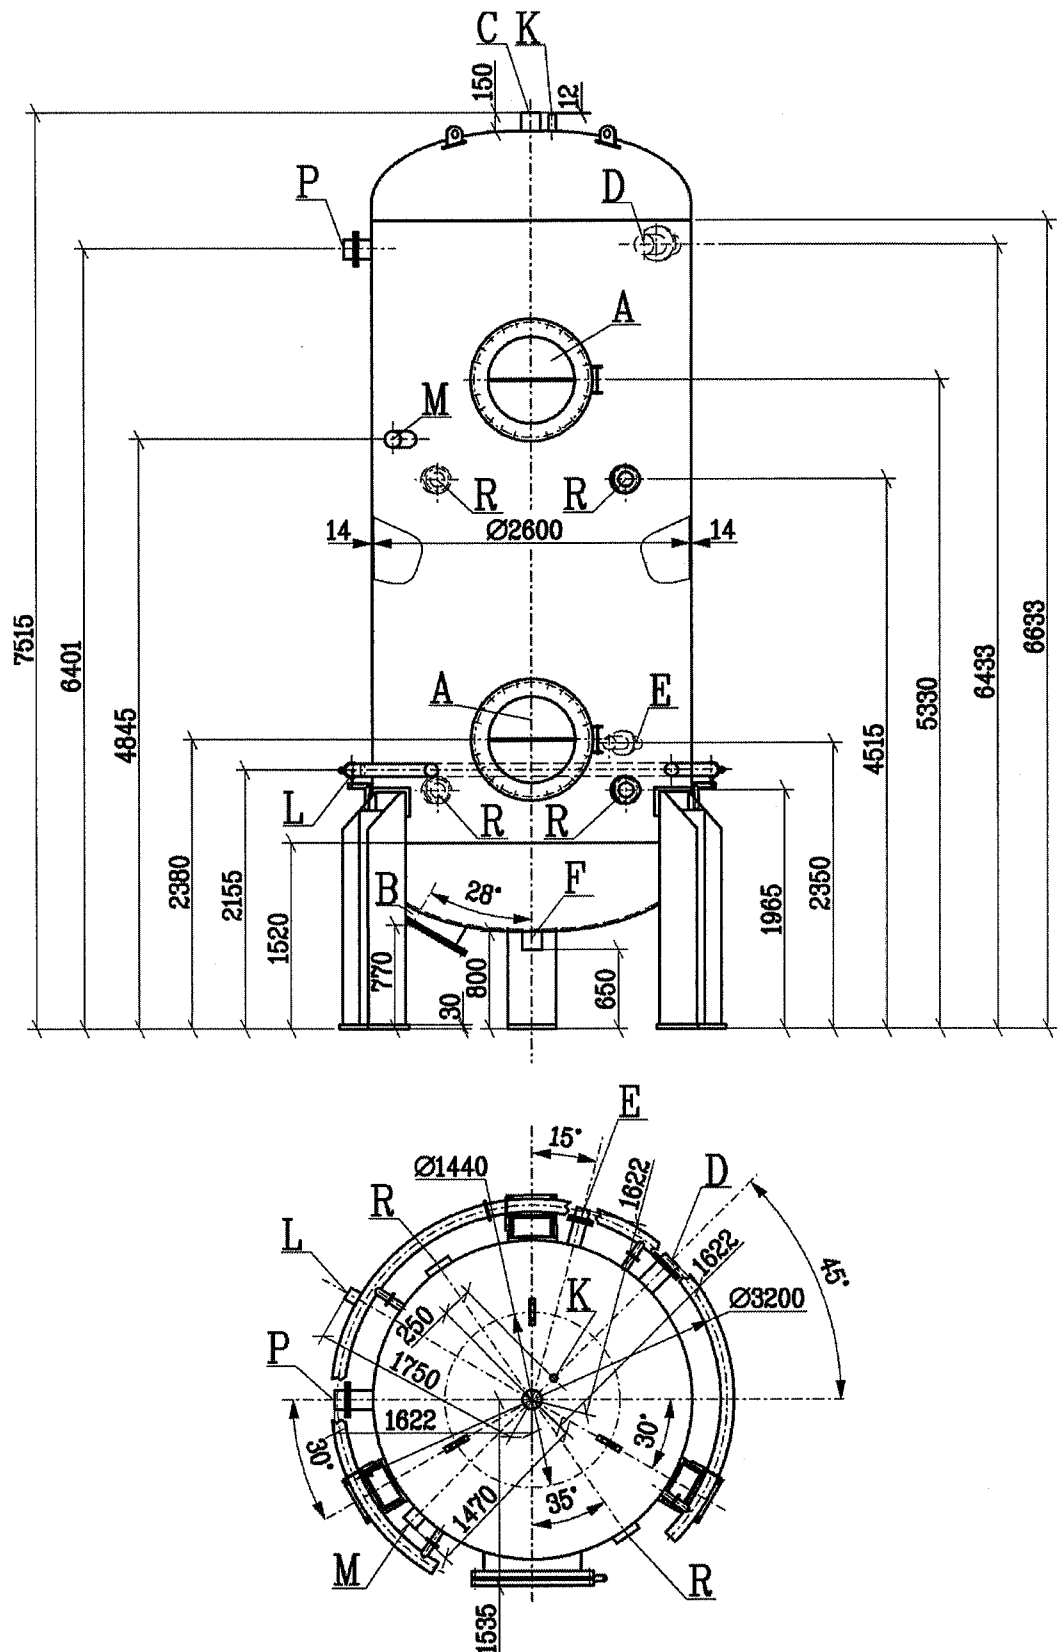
Габаритный чертёж фильтра-регенератора катионита LDP43AT001
